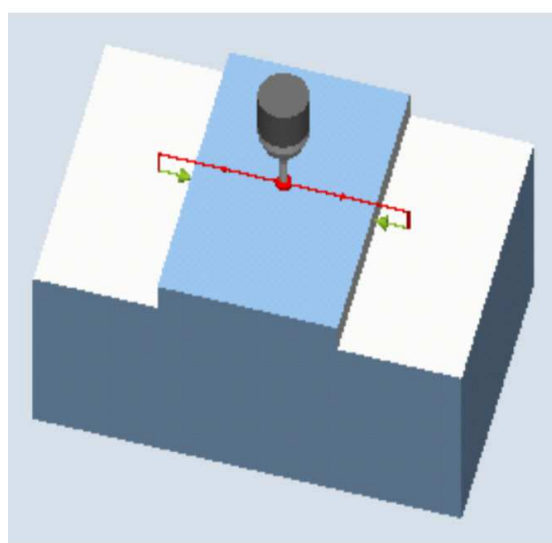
Kompenzace šikmého ustavení obrobku na základě změření úhlu [3]
